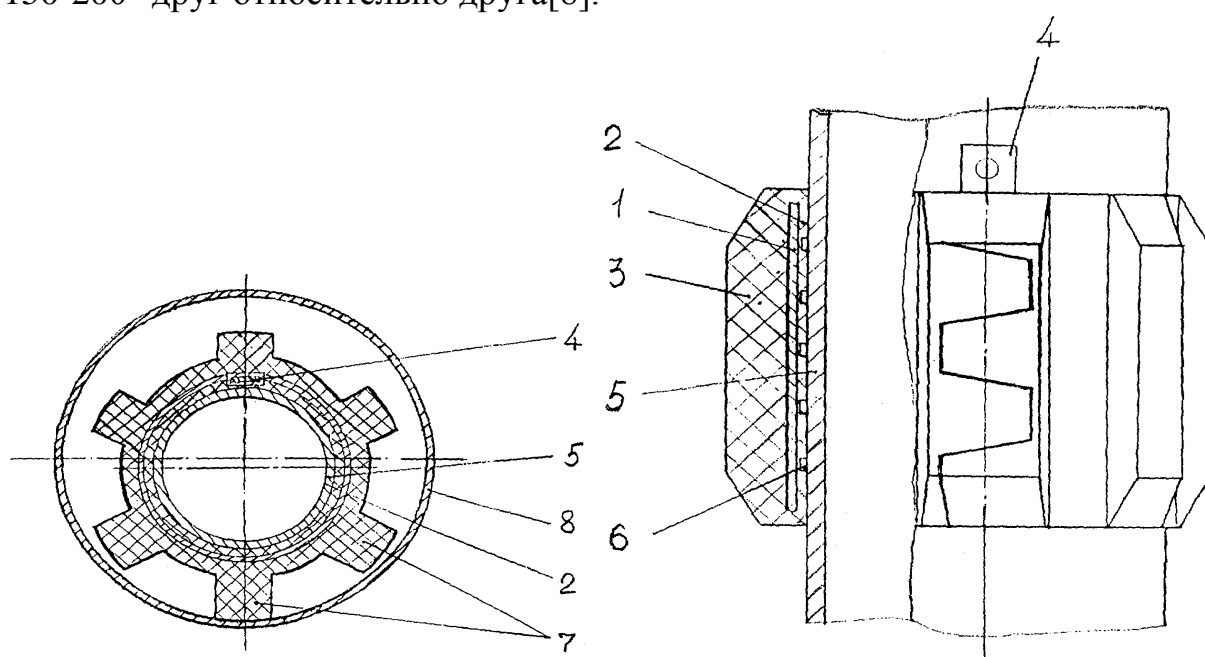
Устройство для предохранения от взаимного истирания труб: 1- металлический корпус, 2 – внутренний эластичный элемент, 3 – наружный эластичный элемент, 4 – механизм запирания, 5 – бурильная труба, 6 – кольцевые канавки, 7 – ребра, 8 – стенка обсадной трубы.
